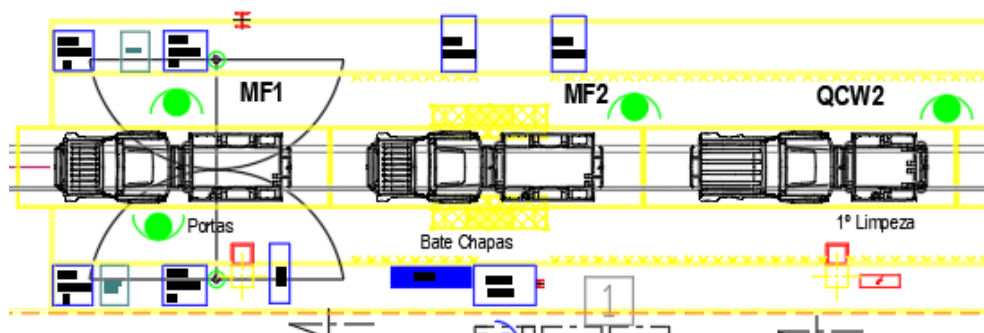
Linha de Soldadura *Metal Finish* (Fonte: Toyota Caetano Portugal)
